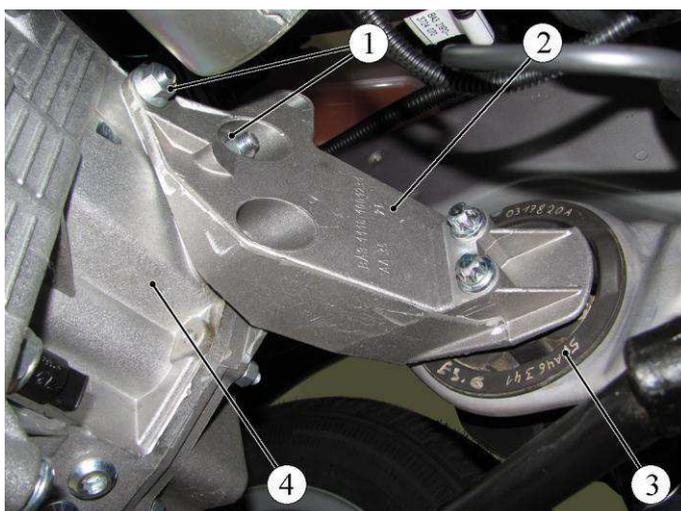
Отсоединение кронштейна левой опоры подвески двигателя от коробки передач:
